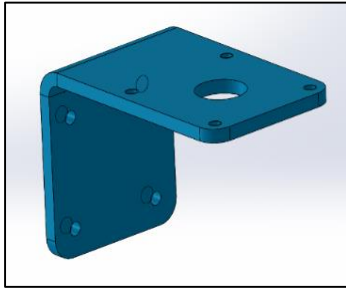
13 : Support du portique et plaque de montage de glissière
